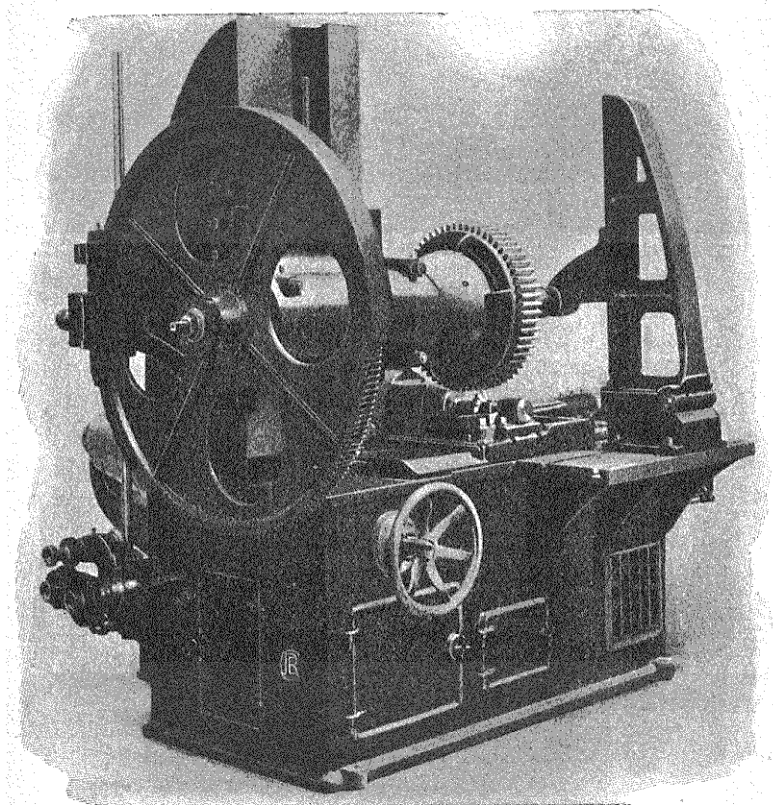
Machine à fraiser automatiquement les engrenages droits Reinecker.
